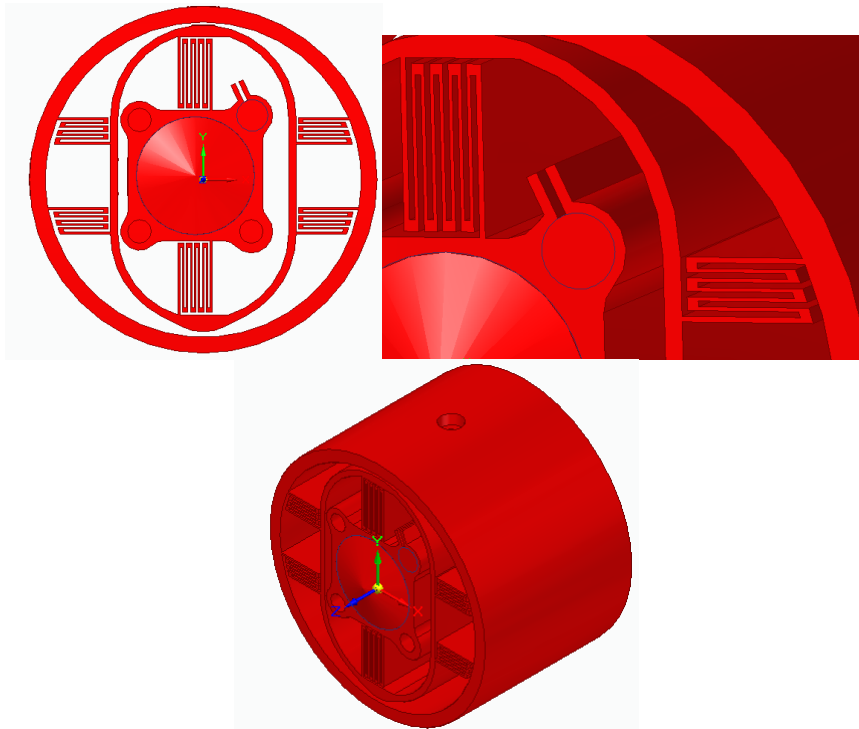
Geometría del prototipo flexural con abrazadera integrada parte superior derecha.
